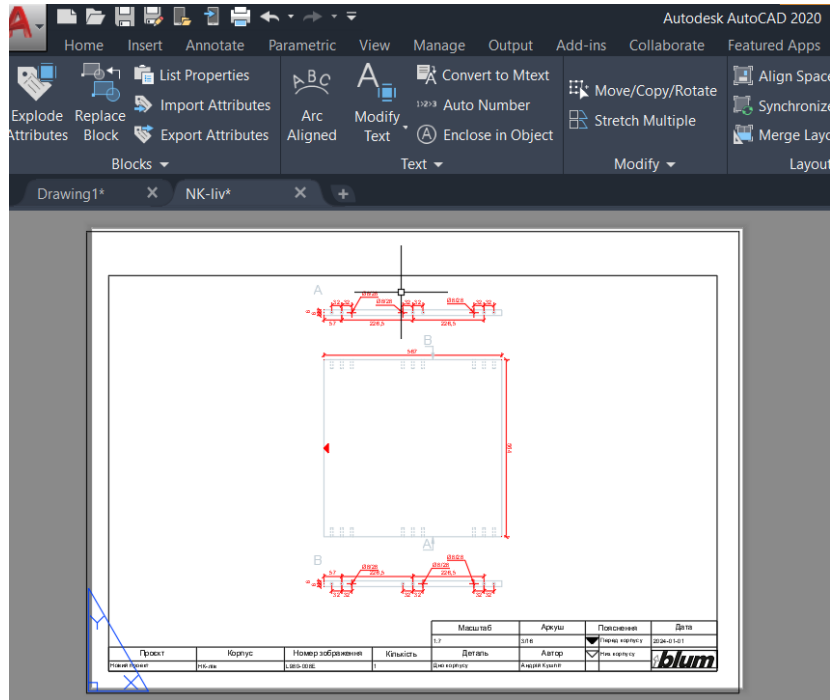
Експортоване в Autocad робоче креслення в форматі DWG
